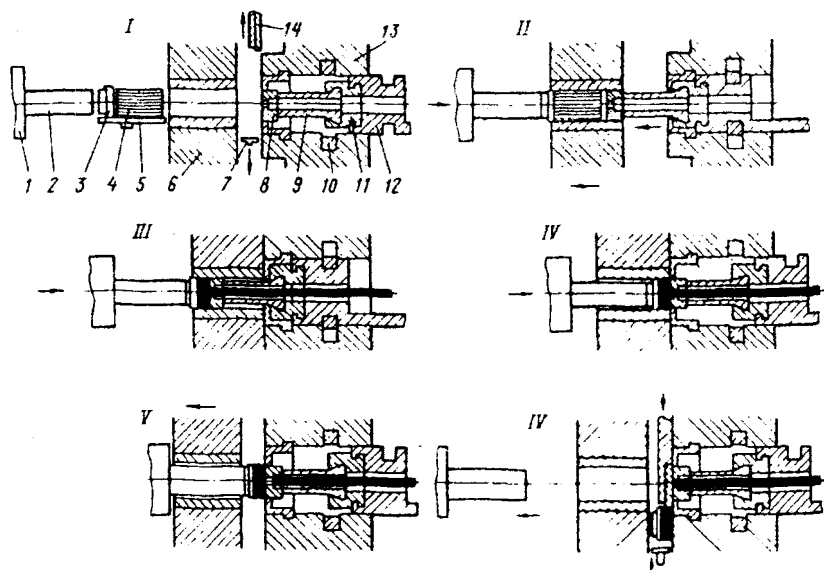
Схема процесса прессования сплошных профилей с обратным истечением металла: 1 - прессующая траверса; 2 - пресс-штемпель; 3 - пресс-шайба; 4 - заготовка; 5 - податчик заготовок; 6 - контейнер; 7 - приемник пресс-остатков; 8 - матрица; 9 - шплинтон; 10 - затвор; 11 - салазки; 12 - мундштук; 13 - передняя поперечина; 14 - ножницы
